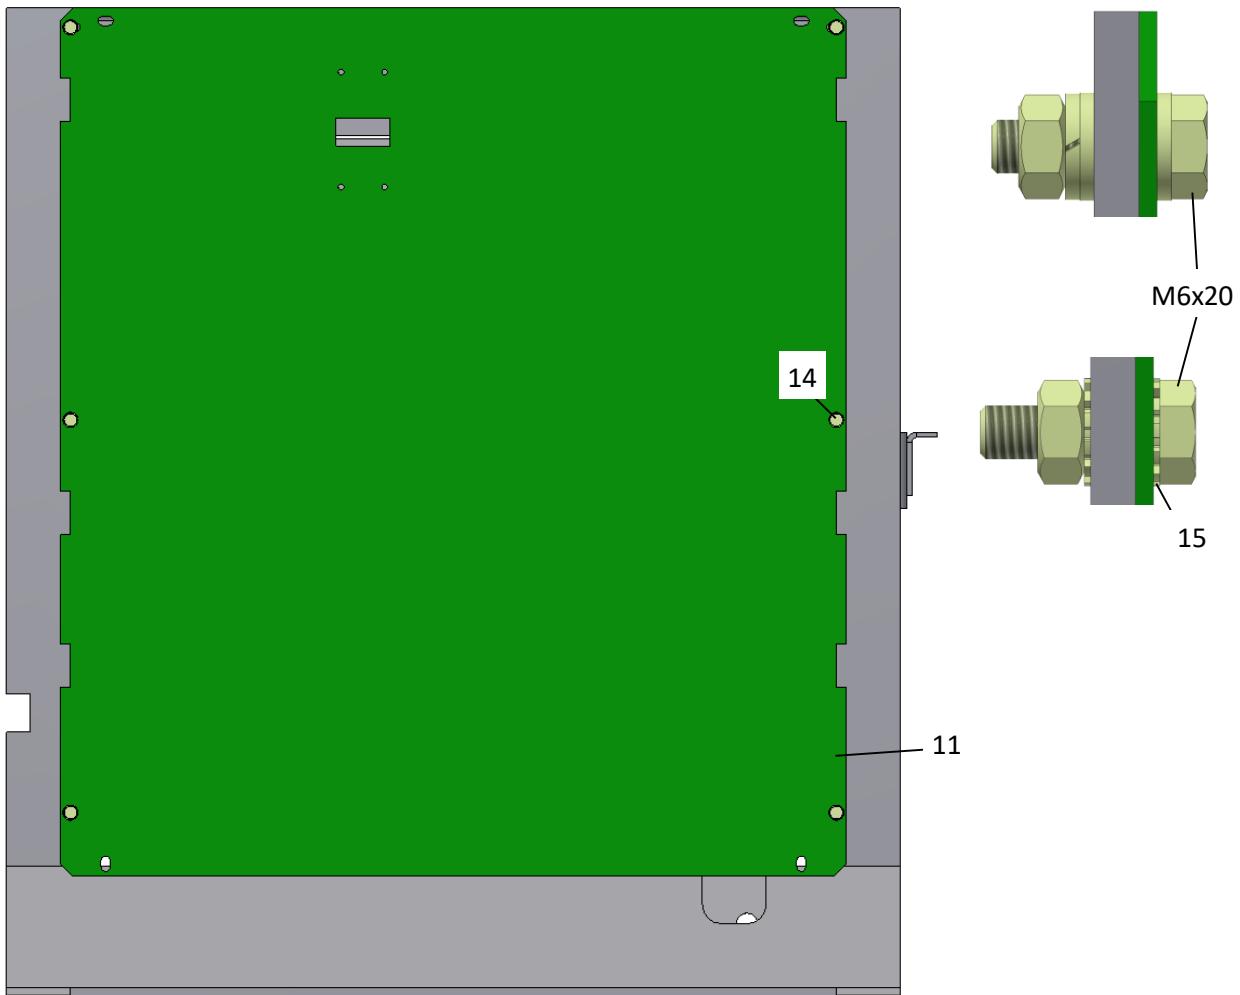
Установка фасадного листа на раму ВМП-10П
